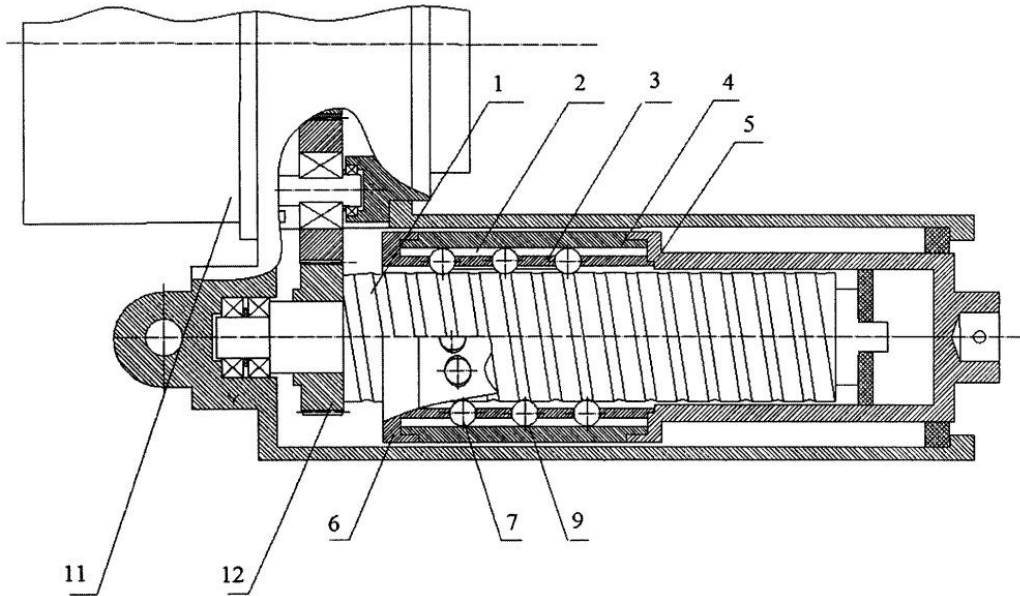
Схема приводу: 1 - гвинт; 2 - гайка; 3 - сепаратор; 4 – корпус сепаратора; 5, 6 – кришки сепаратора; 7 – кульки; 9 – внутрішня частина корпусу редуктора; 11 – електродвигун; 12 – швидкохідна передача.
